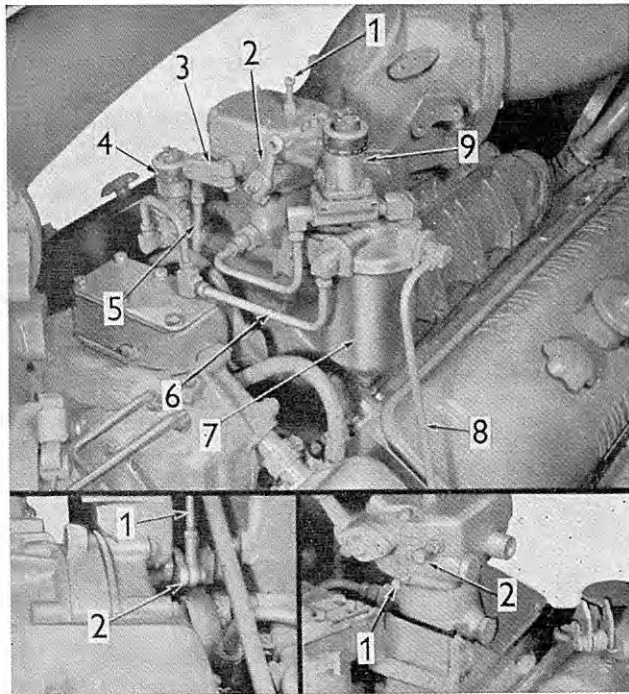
Montage du régulateur hydraulique sur le moteur 16V-71
